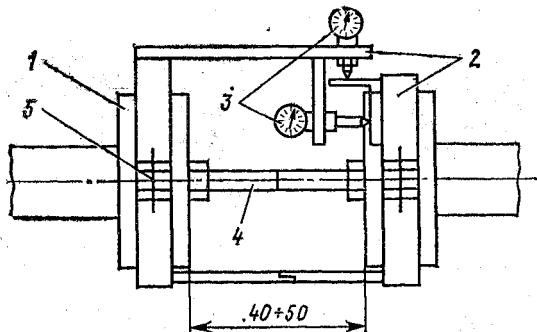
Установка пары радиально-осевых скоб для центровки валов:
